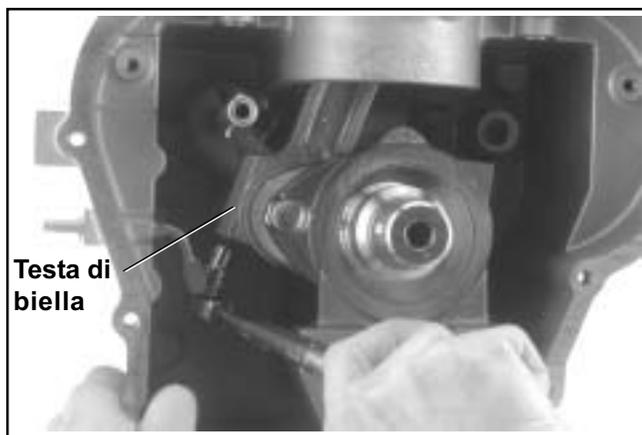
Serraggio dei dispositivi di fissaggio della biella.
